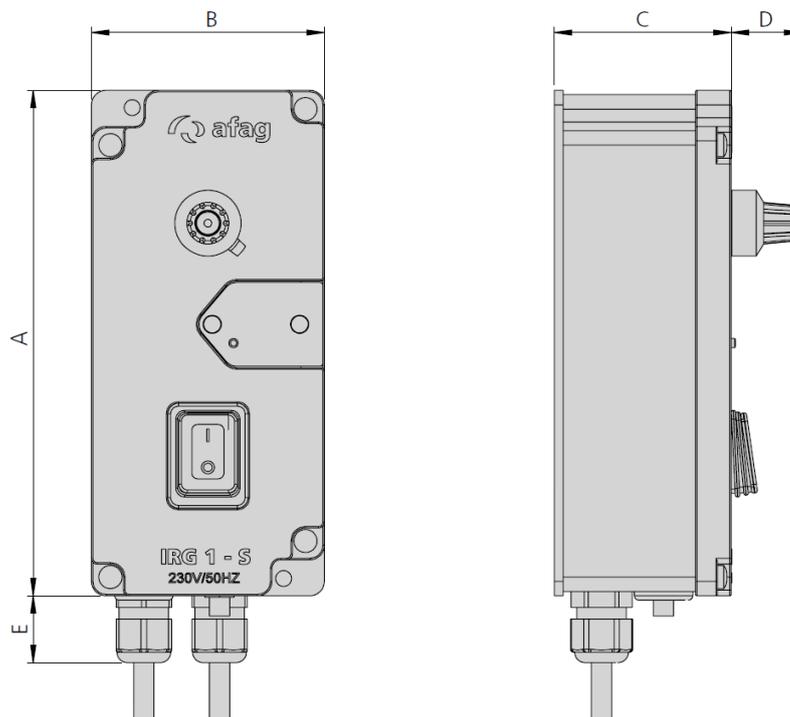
Maßzeichnung Steuergerät IRG1-S
